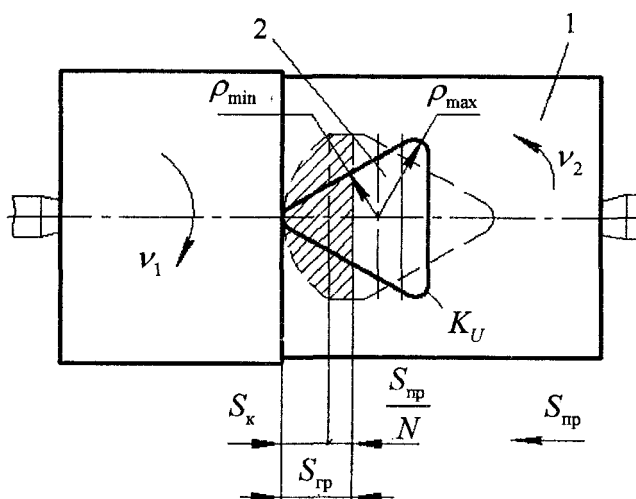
Схема обработки некруглой цилиндрической поверхности вращающимся резцом с полигональной формой режущей кромки
